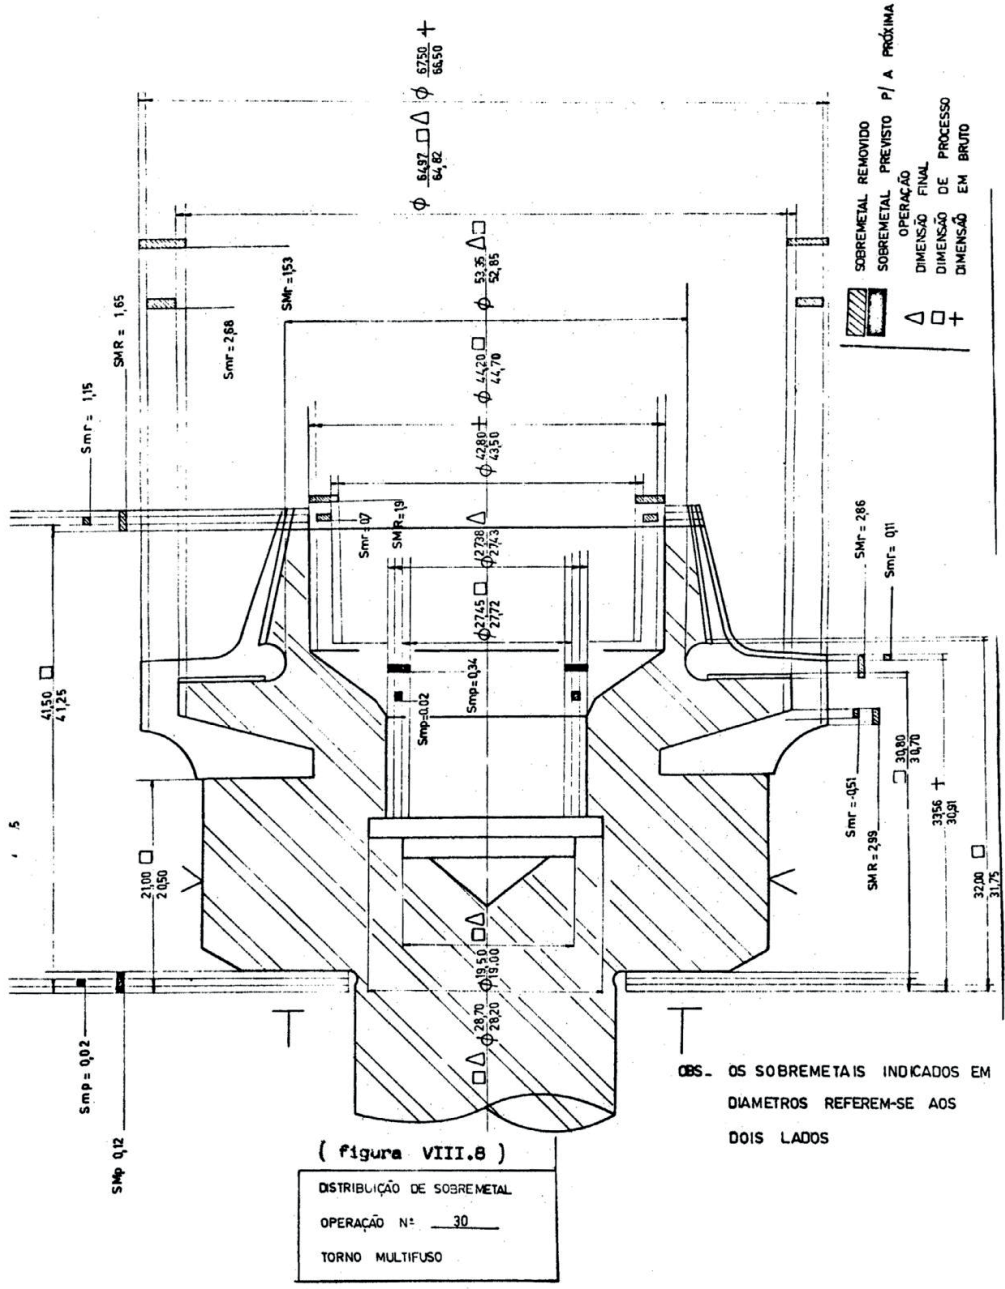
Dimensões a serem observadas e distribuição de sobremetal – operação 30
